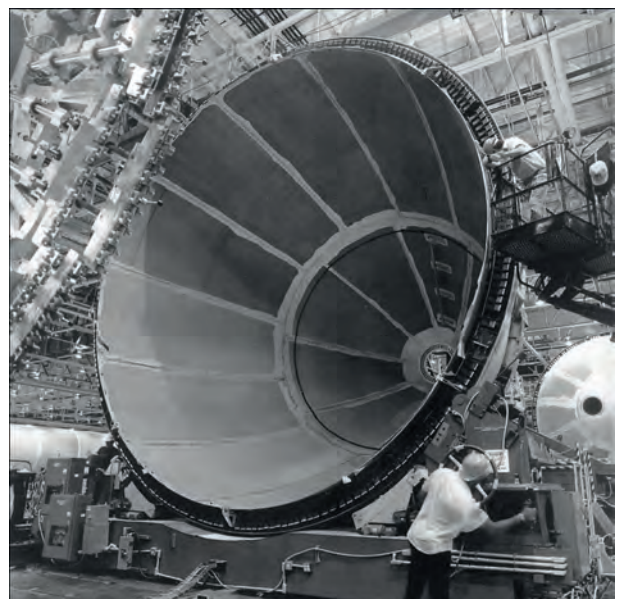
Зварювання купола зовнішнього бака для палива космічного корабля багаторазового використання Space Shuttle (США)
